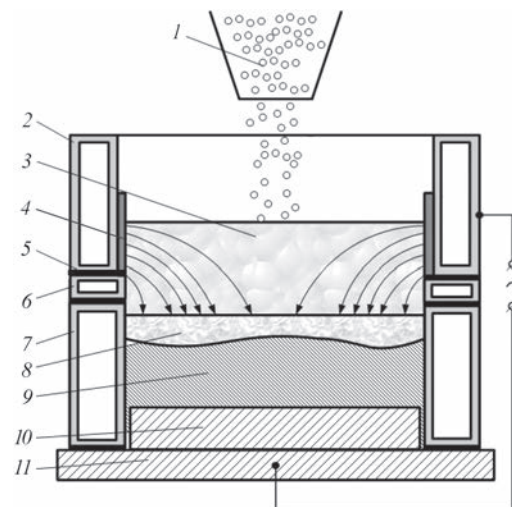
Схема ЕШН дискретною присадкою в СПК: 1 – дискретна присадка; 2, 6, 7 – струмопровідна, проміжна і формуюча секції кристалізатора відповідно; 3 – шлакова ванна; 4 – захисне футерування; 5 – ізоляційна прокладка; 8 – металева ванна; 9 – наплавлений метал; 10 – виріб; 11 – піддон. Стрілки показують розподіл струму в шлаковій ванні
